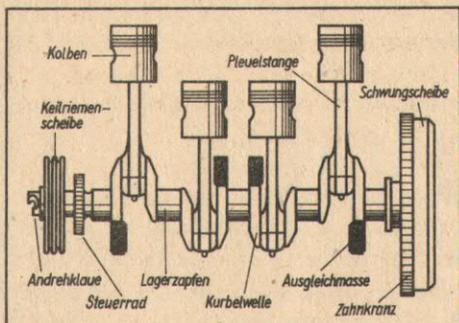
/1 Kurbelgetriebe eines Vierzylindermotors mit fünffach gelagerter Kurbelwelle
